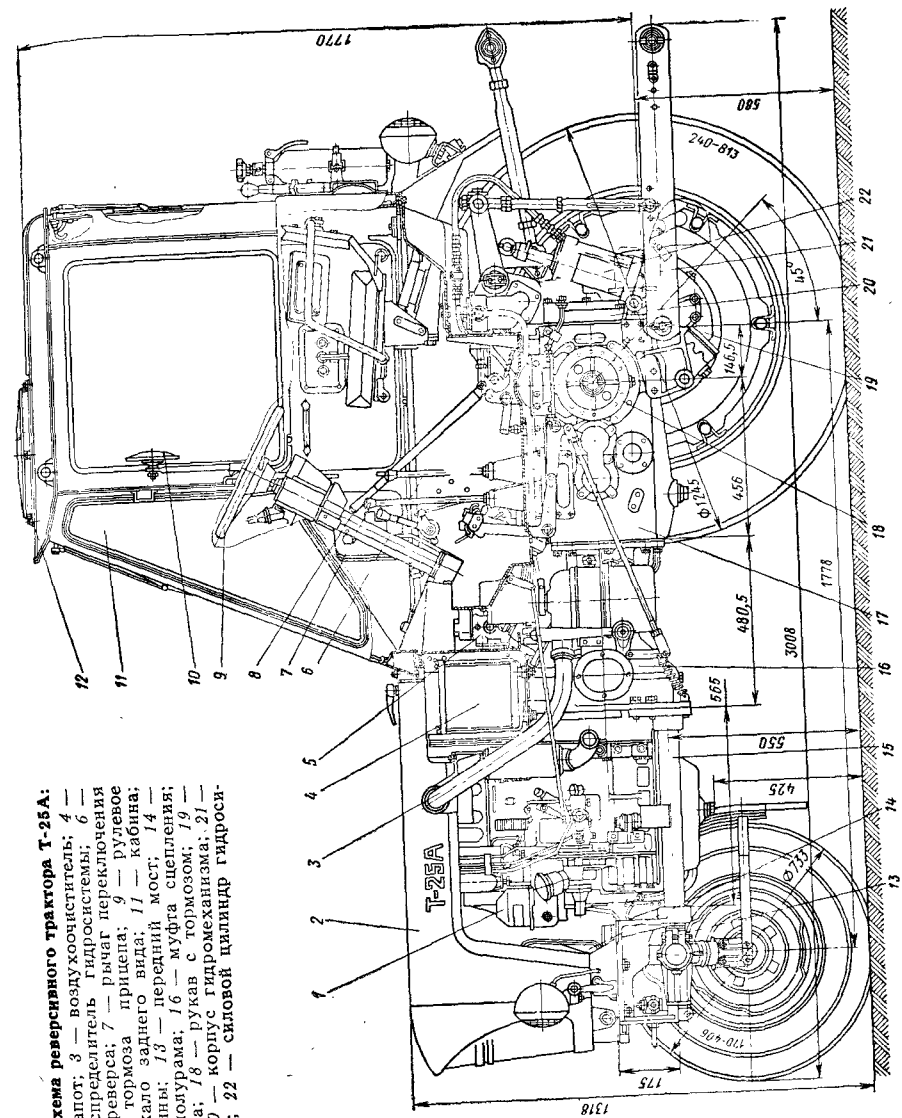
Размерная схема реверсивного трактора Т-25А:
